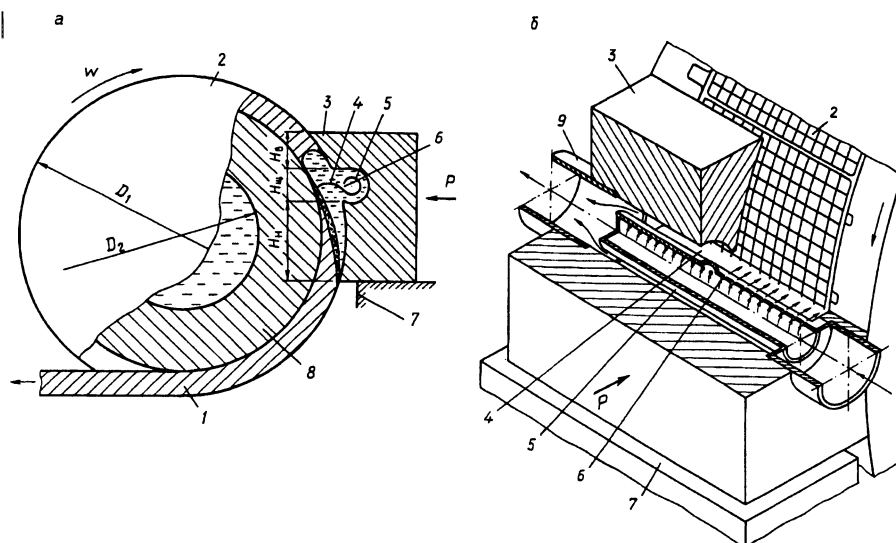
Принципиальная схема (а) и конструкция (б) кристаллизатора машины непрерывного литья аккумуляторной решетки: 1 — отливка; 2 — формообразующий валок; 3 — башмак-питатель; 4 — литниковый паз; 5 — литник-распределитель; 6 — литниковое отверстие; 7 — неподвижная опора; 8 — вода; 9 — сливная труба
